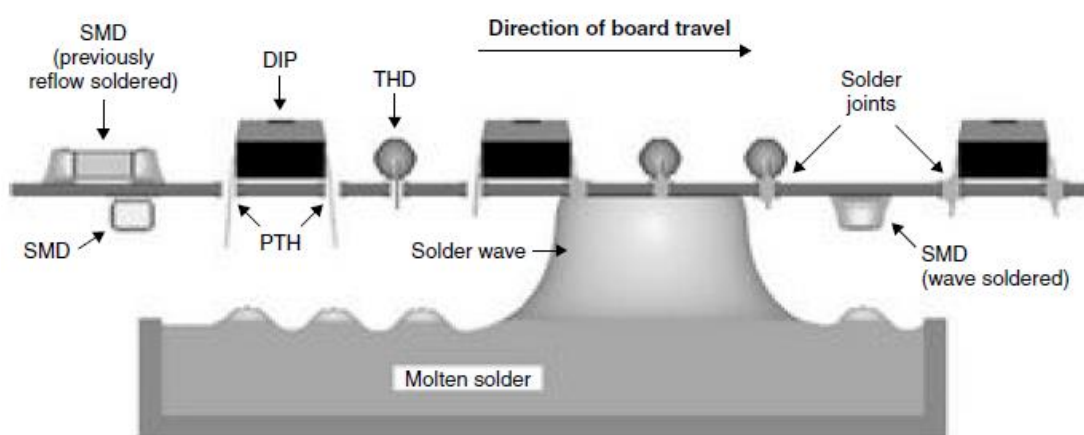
Cadena de montaje de PCB (Mitzner, 2009)
